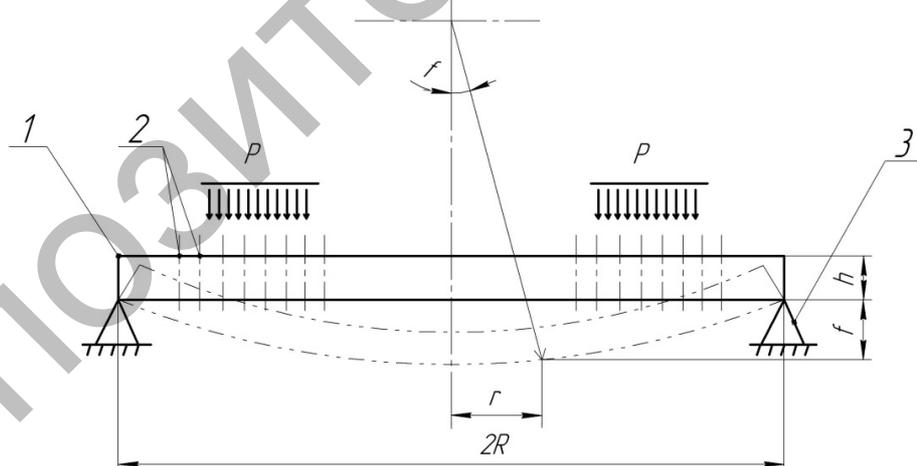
Схема деформаций корпуса сплошной матрицы с шарнирным закреплением по наружному контуру
